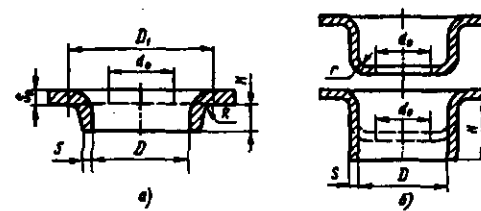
Схемы отбортовки плоской заготовки (а) и заготовки, полученной вытяжкой (б)
